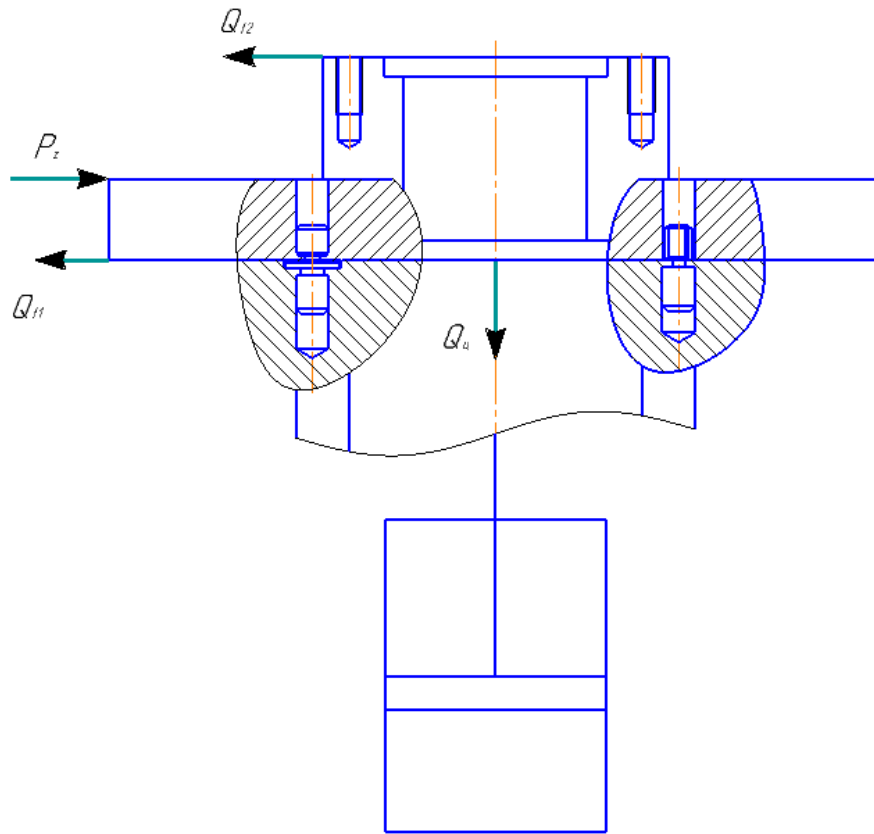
Розрахункова схема пристосування для фрезерування
